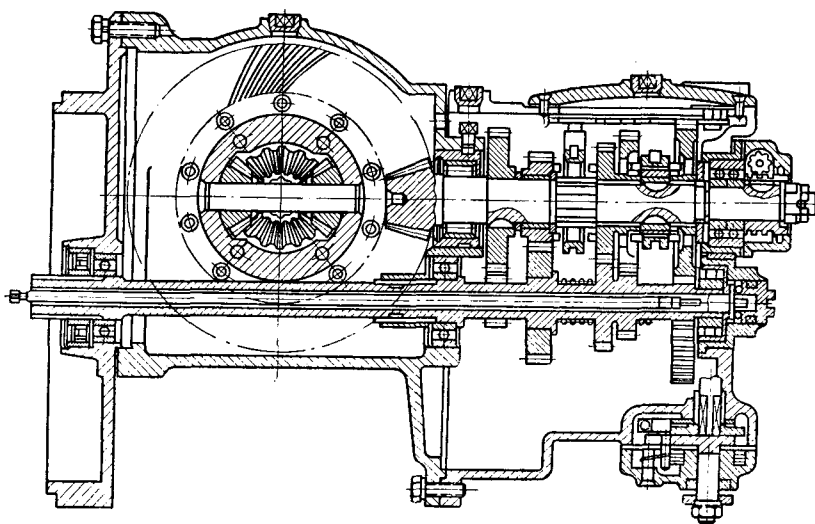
Четырехступенчатая коробка передач рекордного автомобиля «Звезда» (рабочий объем 350 см³) с задним расположением двигателя.
